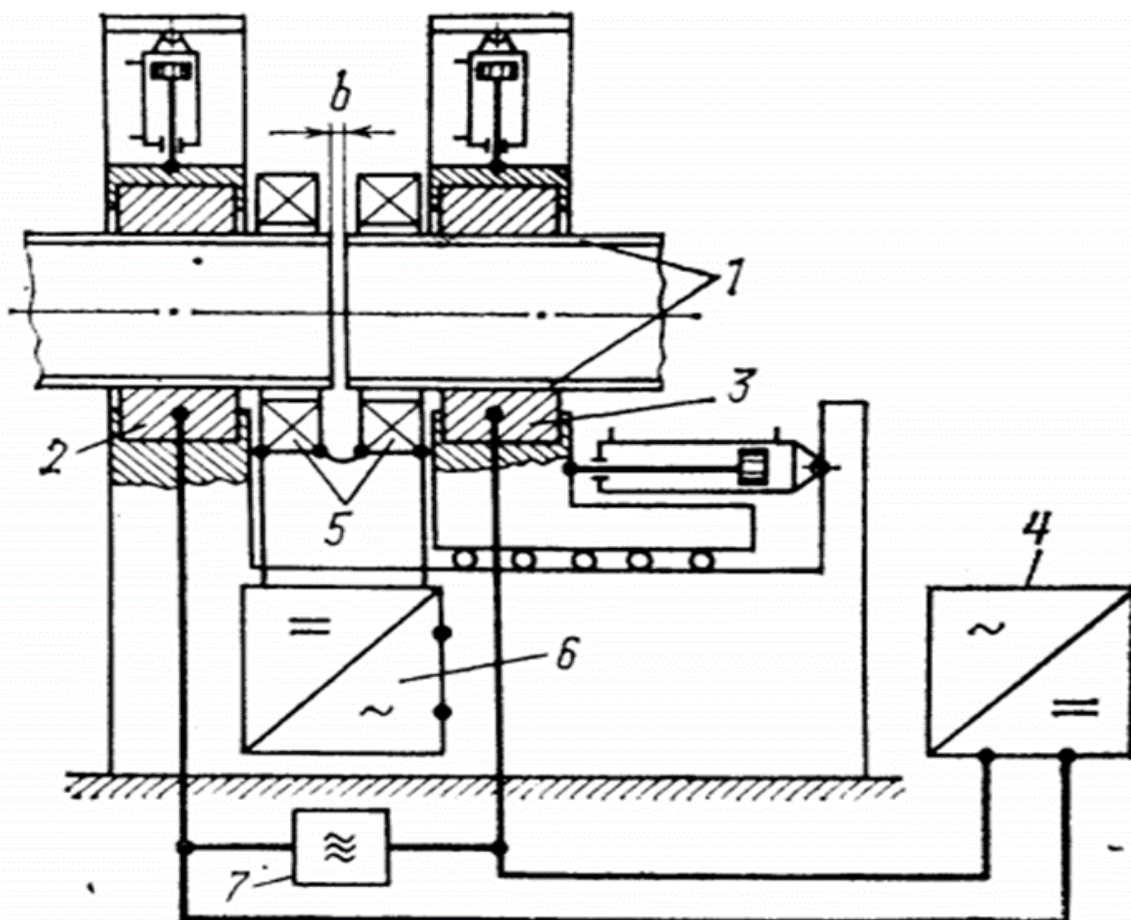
Схема установки ЗДМП: 1– зварювані труби 2, 3– затискні пристрої (струмопідводи); 4– джерело живлення дуги; 5– електромагніти; 6– джерело живлення електромагнітів; 7– джерело запалювання дуги
